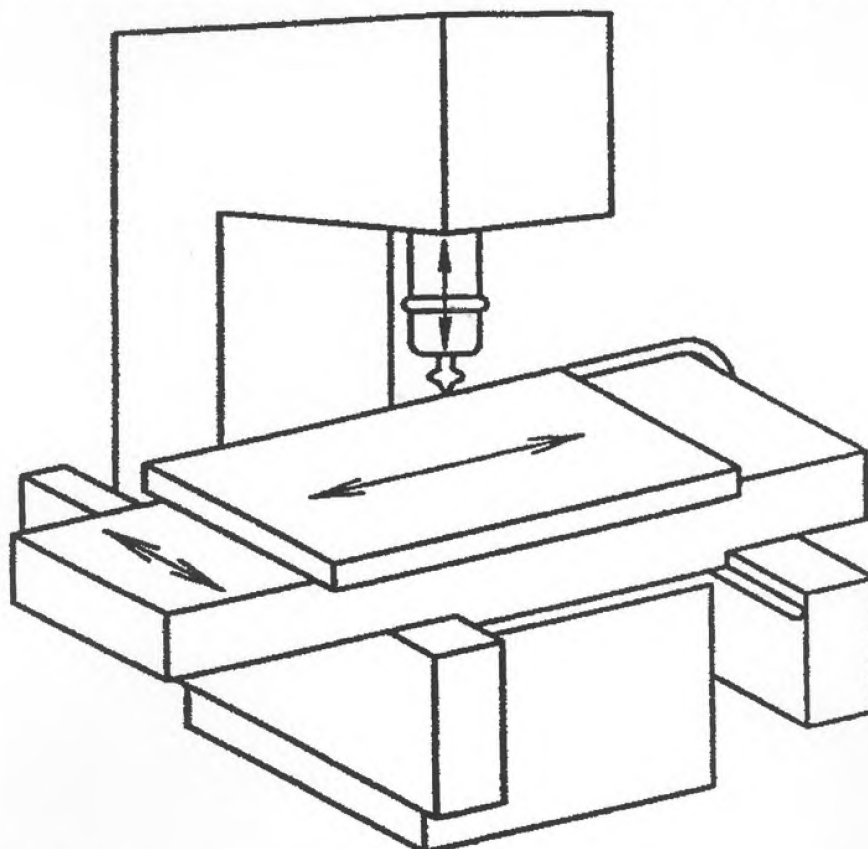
Фрезерный станок с верхним расположением шпинделя (подвижный стол)¹
